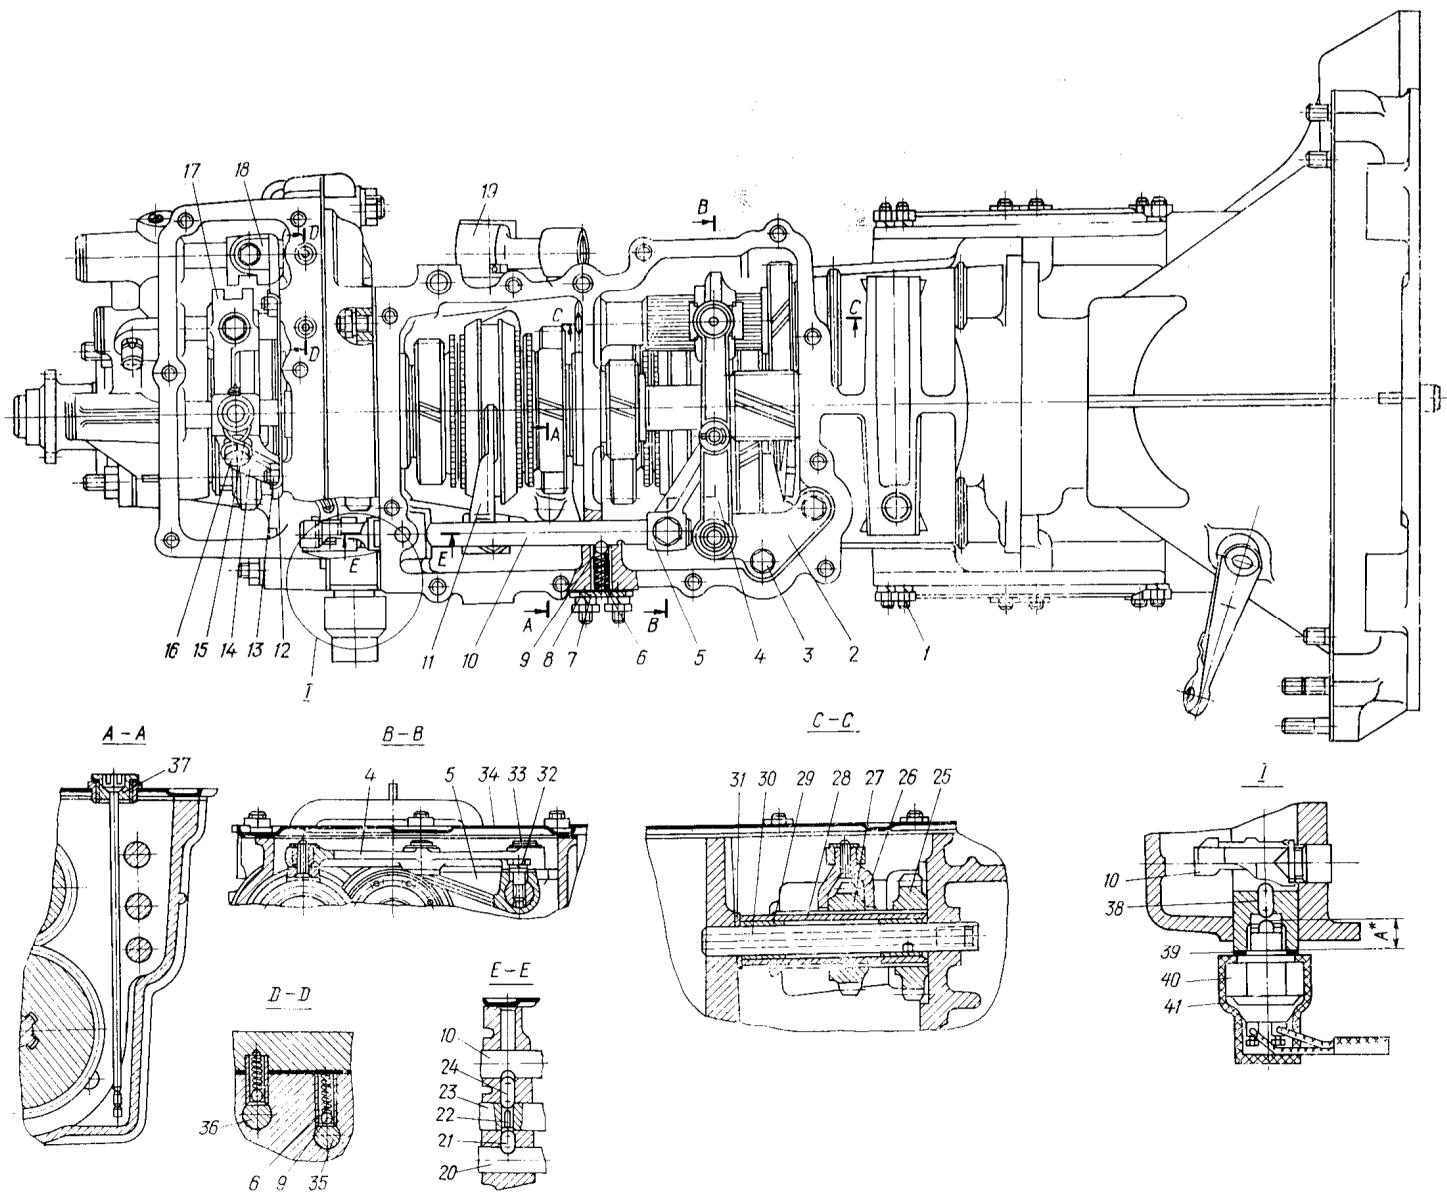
Коробка передач (вид сверху, верхняя крышка снята):
